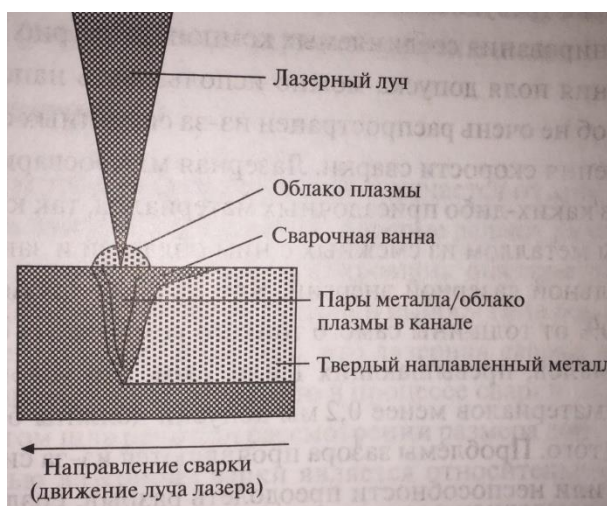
Основы лазерной сварки в режиме канала или глубокого проплавления
